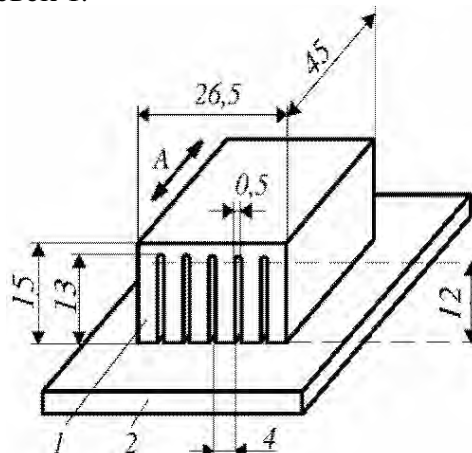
Схема изготовления пьезодатчиков из кварца
